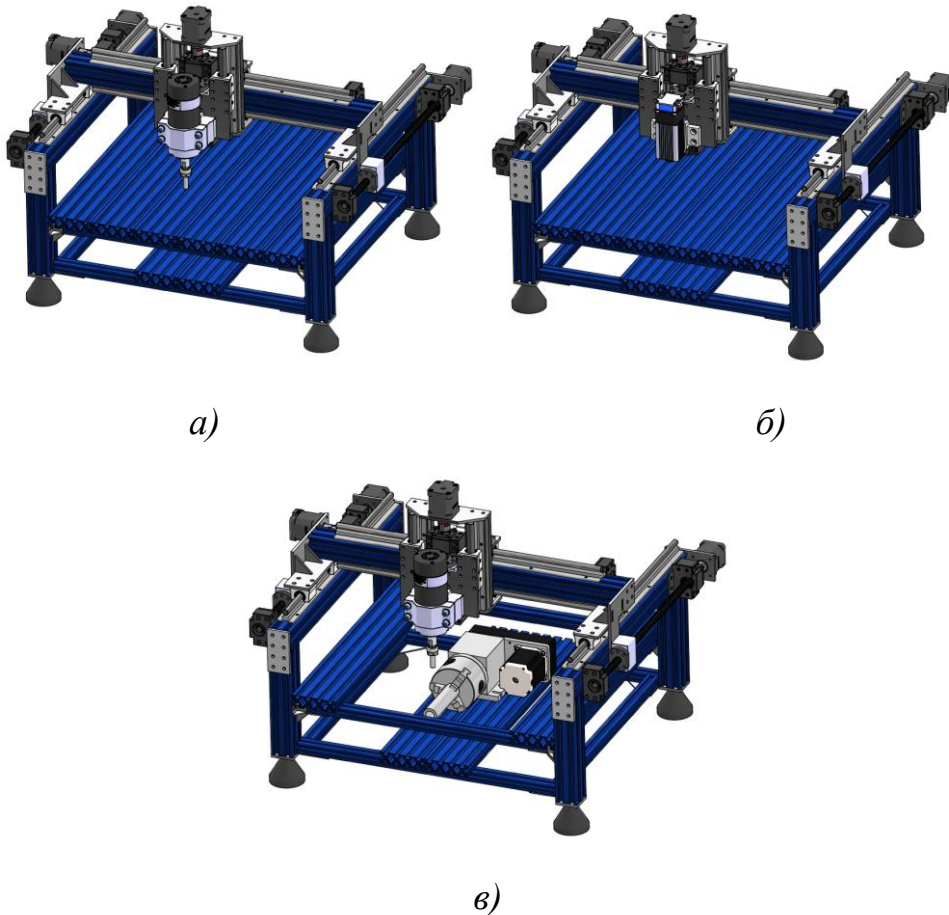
Варіанти створеного верстат: а) - фрезерний верстат; б) - лазерний верстат; в) - фрезерний 4-х координатний верстат
